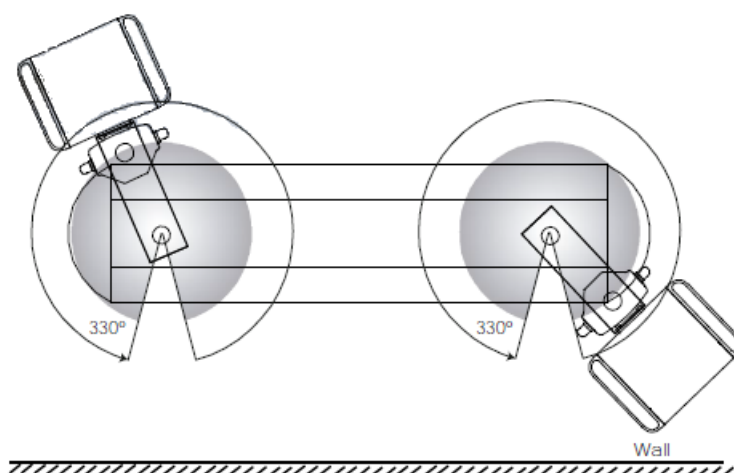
Plage de pivotement des bras d'extension sur une section ABITUS
